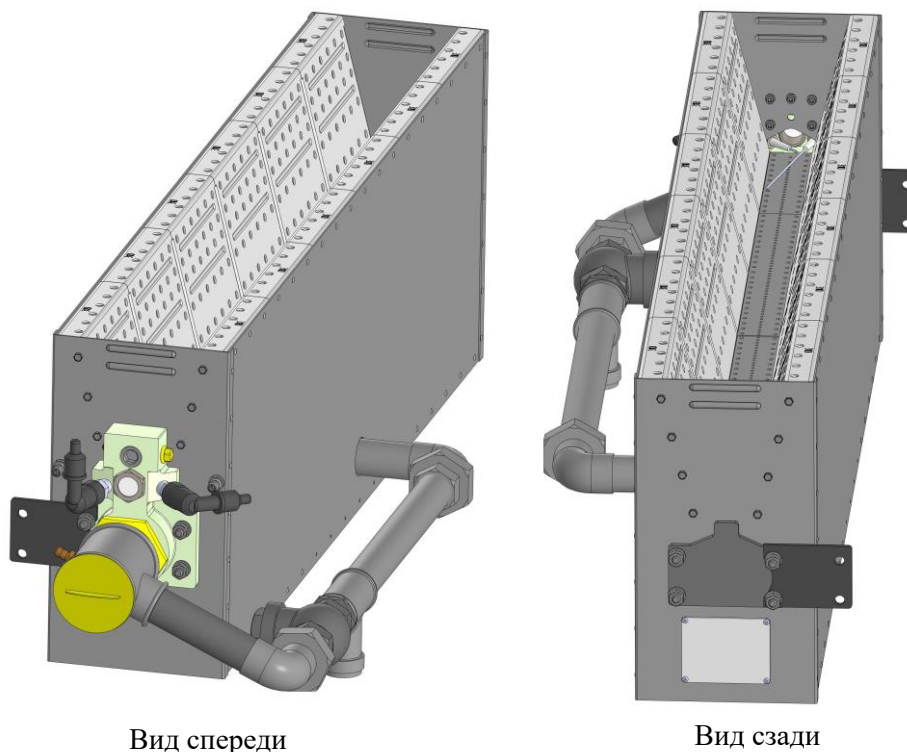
Внешний вид горелки газовой ТЕРМОПОТОК 700
